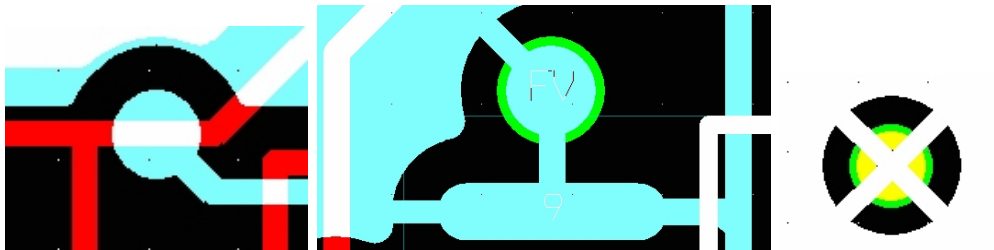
Alcune regole per la corretta progettazione del Layout di una PCB
